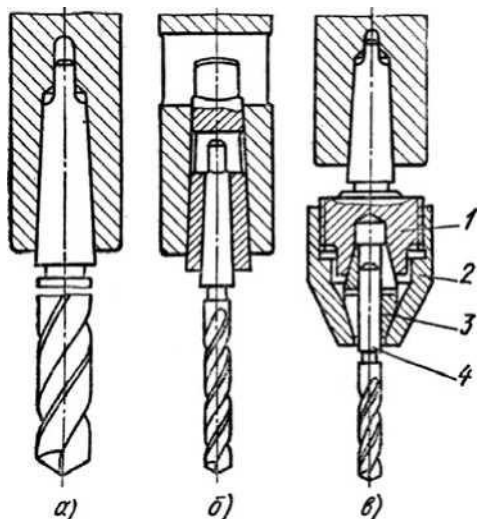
Закрепление инструмента на сверлильных станках: а - шпиндель; б - коническая втулка; в - цанговый патрон; 1 - корпус патрона; 2 - втулка; 3 - цанга; 4 - хвостовик инструмента
